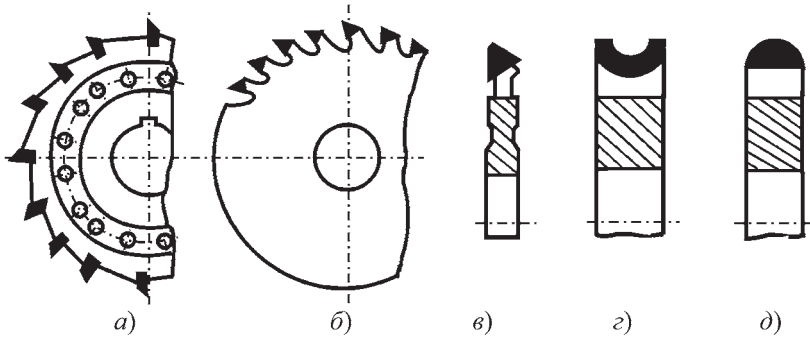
Дисковые фрезы, оснащенные режущими элементами из ПСТМ: а — фреза; б — пила; в–д — фрезы со специальной формой режущей части
